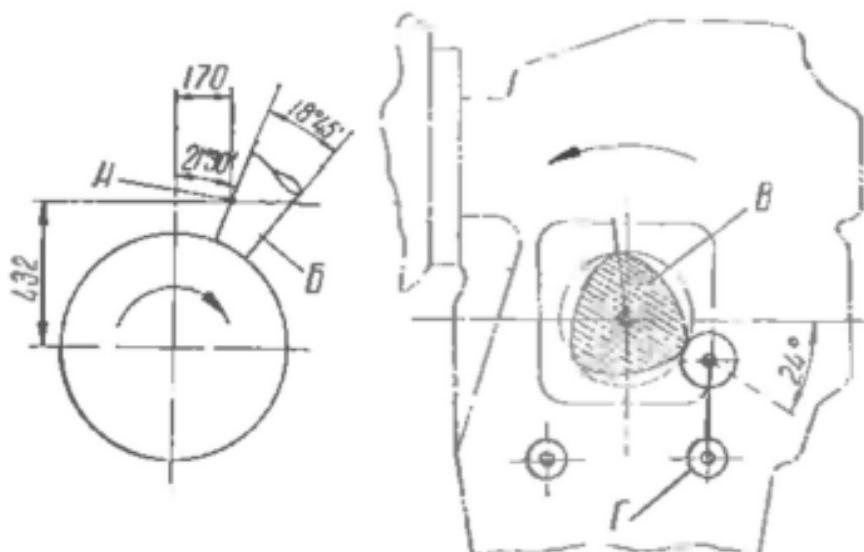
Положение лопасти винта при регулировке выстрела левого пулемета ШКАС (вид против полета) и положение кулачковой шайбы (вид с левого борта на левый синхронизатор).
